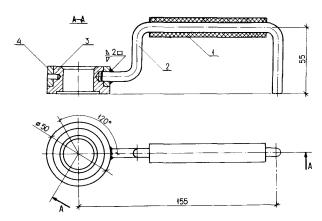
Общий вид приспособления 1 - резиновая ручка; 2 - ручка; 3 - кольпо: - обойма
